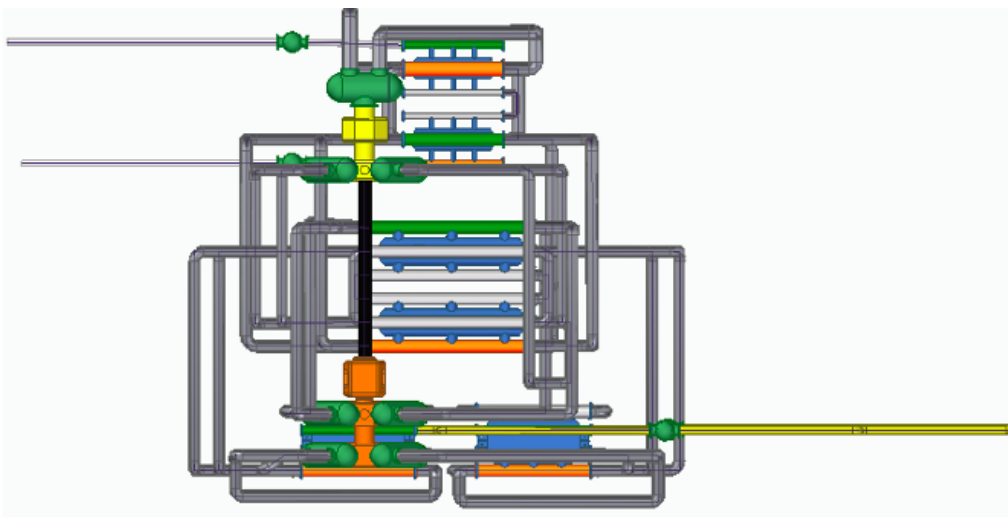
Vista Planta versión extendida (Fuente: Elaboración propia)
